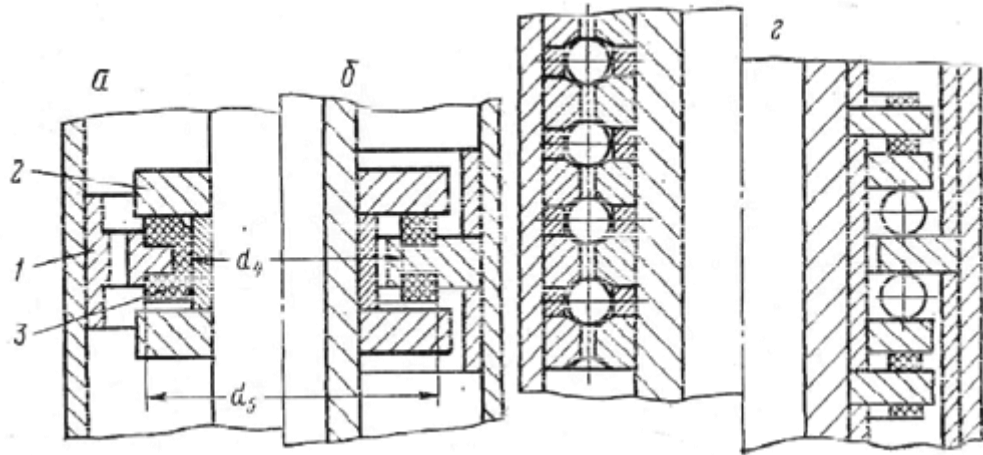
Резинометалеві підшипники (а, б) та опори кочення (в, г)
